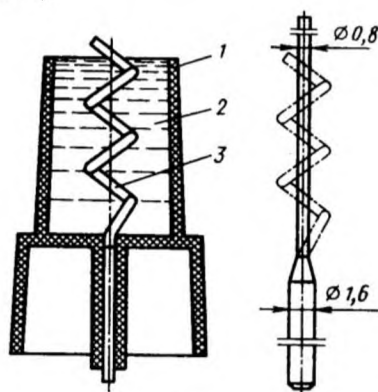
Патрон для электрогидравлической развальцовки: 1 – полиэтиленовый корпус; 2 – жидкий заполнитель; 3 – иницилирующая проволока из алюминия
